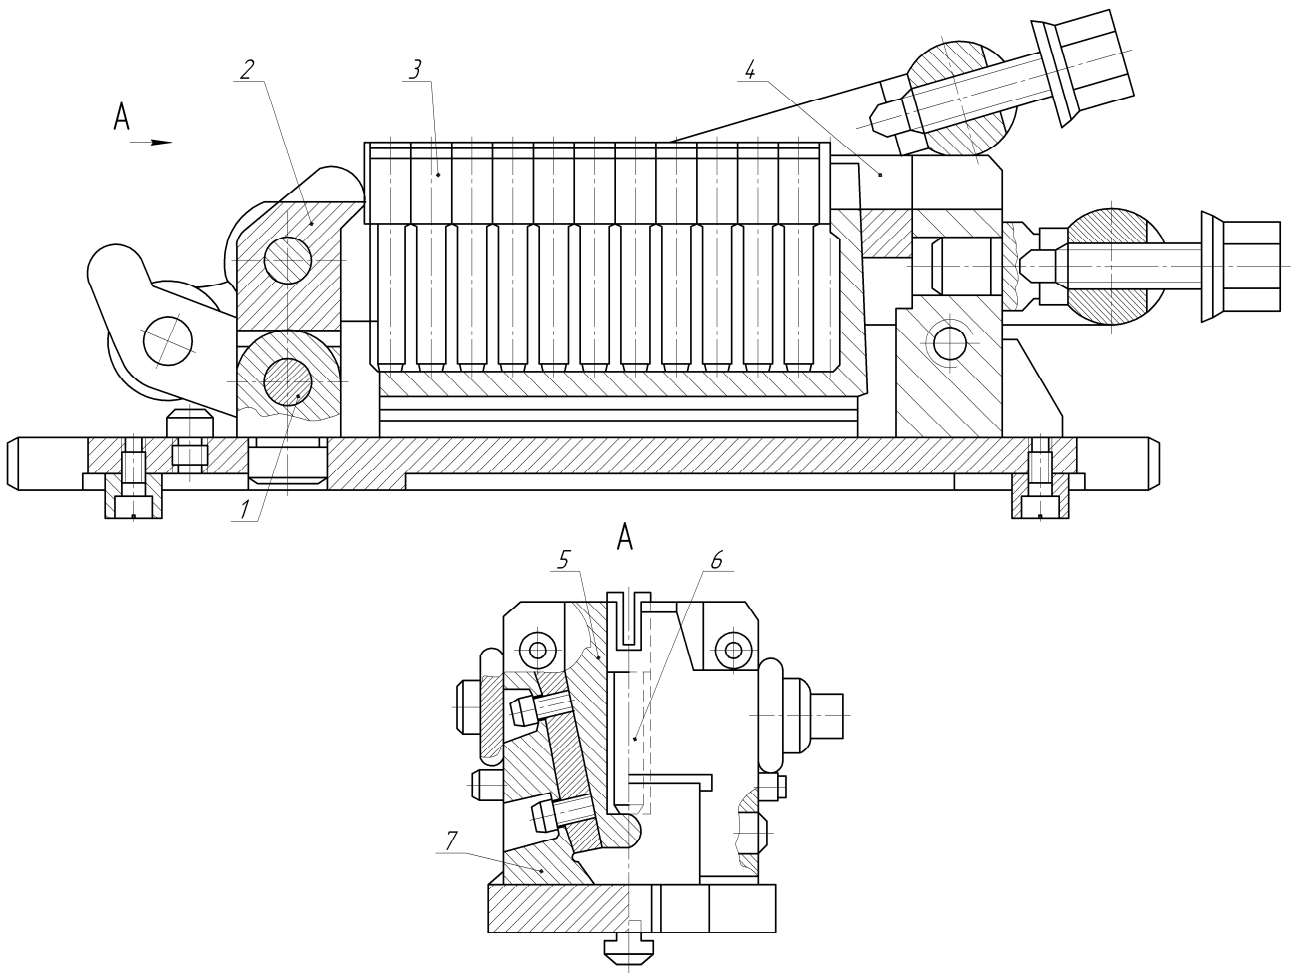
Будова касетного пристрою: 1 – вісь; 2 – прихоплювач; 3 – заготовітка; 4 – упор; 5 – касета; 6 – пластина; 7 – корпус
